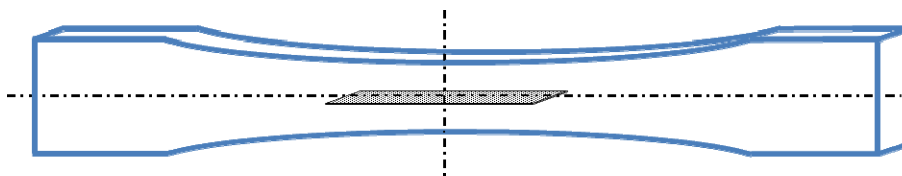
Схема образца (в центре обозначено сечение для изготовления шлифов)
